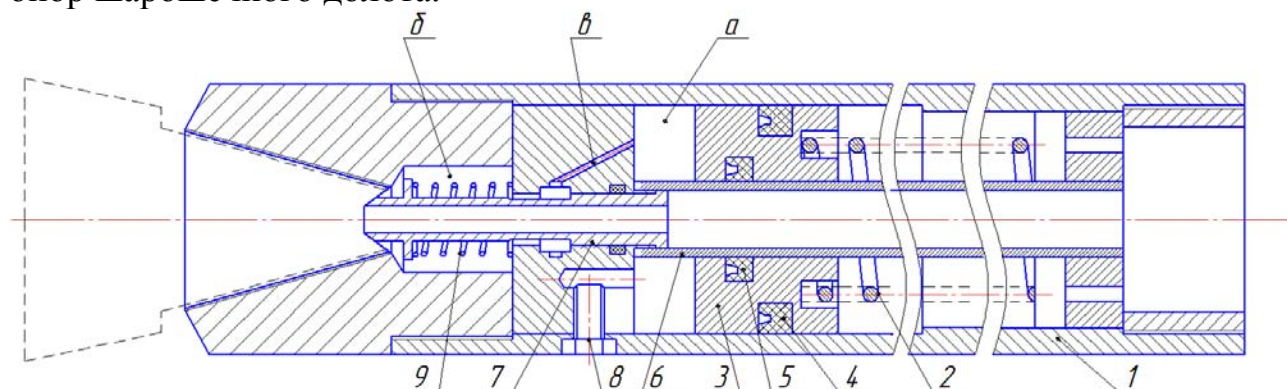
Схема лубрикатора для консистентной смазки подшипников опор шарошечного долота:
